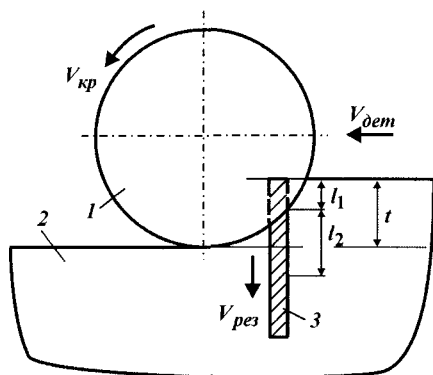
Расчетная схема процесса шлифования: 1 – шлифовальный круг; 2 – обрабатываемая деталь; 3 – адиабатический стержень.
